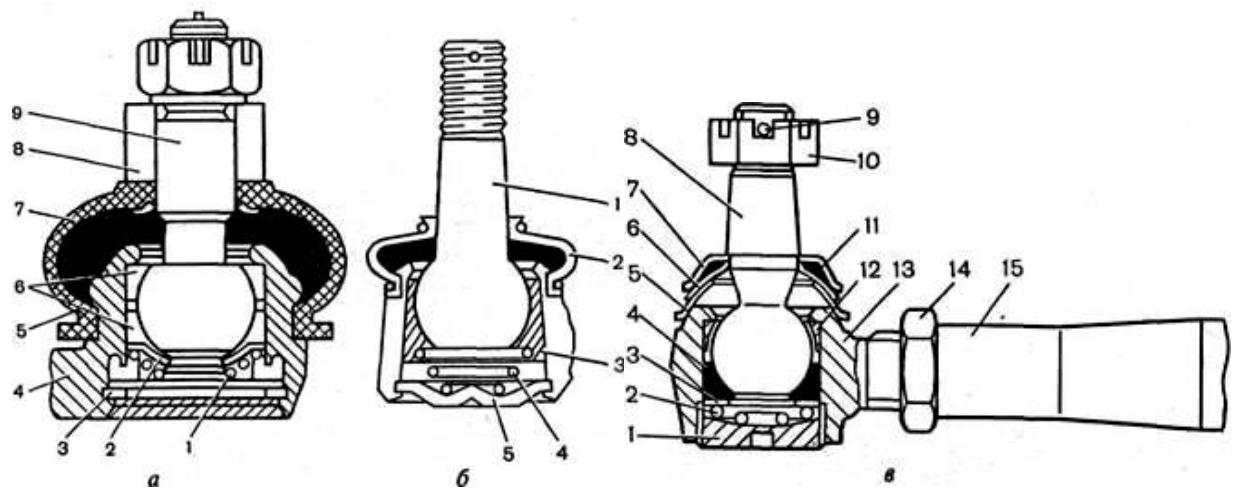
Шарниры рулевых тяг:*a* — автомобиля ИЖ-2715: 1 — пружина; 2 — нажимная обойма; 3 — стопорное кольцо; 4 — рулевая тяга; 5 — пружинное кольцо; 6 — опорный вкладыш; 7 — защитный чехол; 8 — поворотный рычаг; 9 — палец шарнира;*б* — автомобиля ВАЗ-2109: 1 — палец шарового шарнира; 2 — защитный колпачок; 3 — вкладыш шарового пальца; 4 — пружина; 5 — стопорная шайба;*в* — автомобиля УАЗ-31512: 1 — заглушка; 2 — пружина; 3 — пята; 4 — вкладыш; 5 — нижняя сферическая шайба; 6 — верхняя сферическая шайба; 7 — пружинный колпачок; 8 — палец; 9 — шплинт; 10 — гайка; 11 — защитное кольцо; 12 — сухарь; 13 — наконечник; 14 — гайка; 15 — рулевая тяга.
